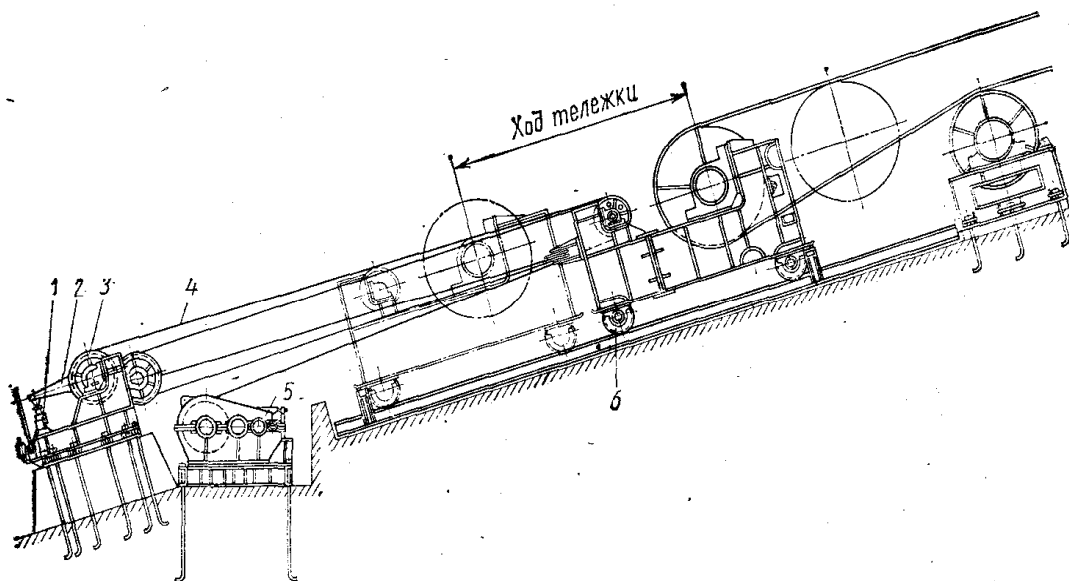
Натяжное устройство с автоматической регулировкой натяжения ленты
